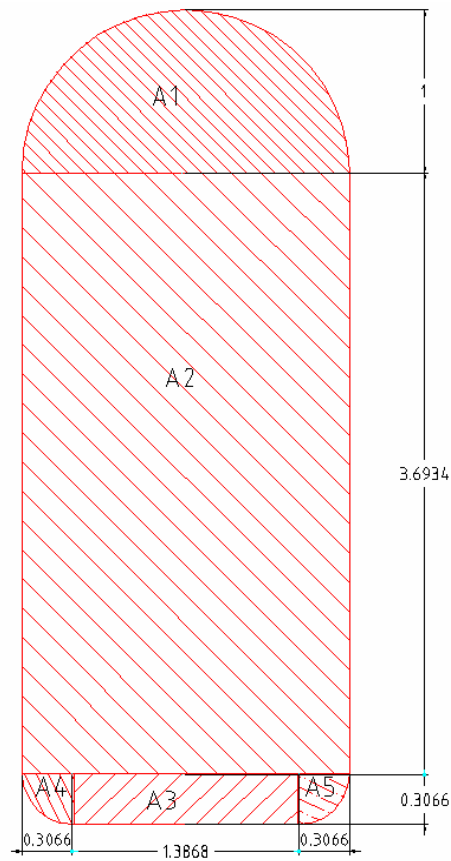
Vista en planta de la superficie del colchón de aire
